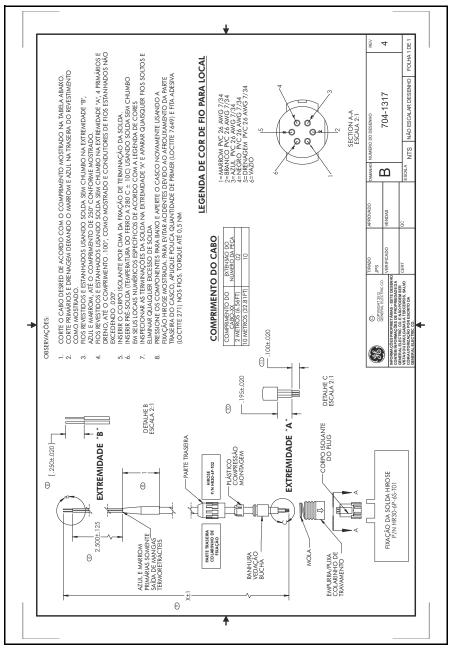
Cabo, Padrão (ref. des. 704-1317, FL 2 de 2)
